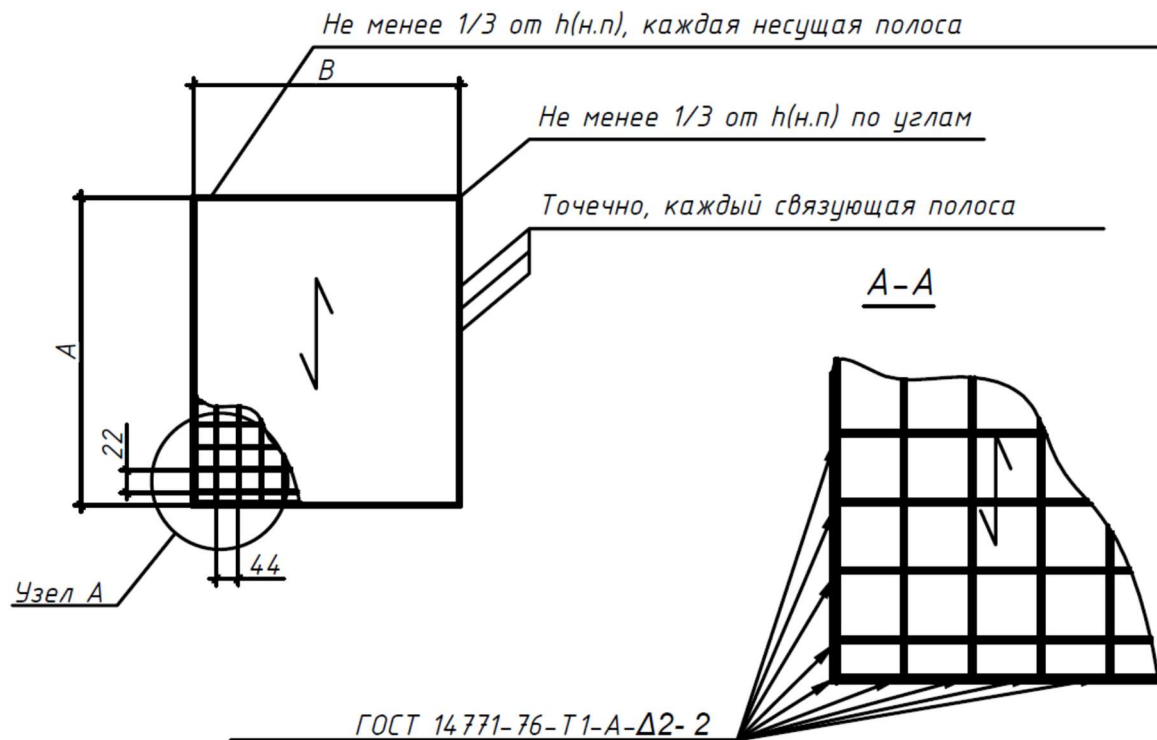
Схема приварки обрамления на щитах прессованного настила
